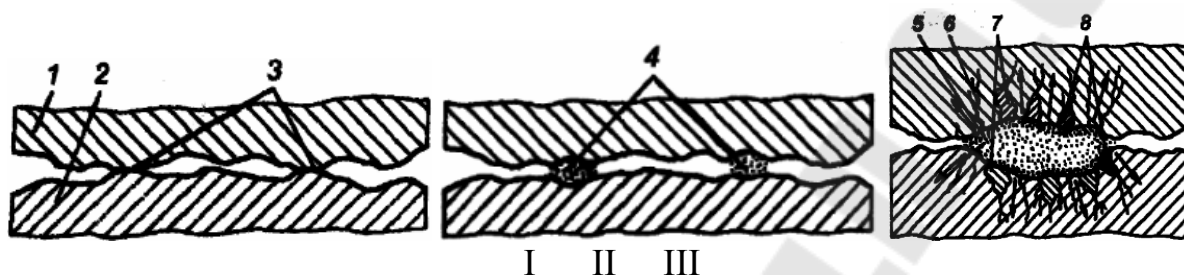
Механизм изнашивания металлических поверхностей при фреттинг-коррозии: 1,2 – контактирующие детали; 3 – точки контакта поверхностей; 4 – мелкие зарождающиеся каверны; 5 – общая большая каверна; 6 – трещины; 7 – отколовшиеся объемы металла; 8 – отколовшиеся частицы с твердой структурой
